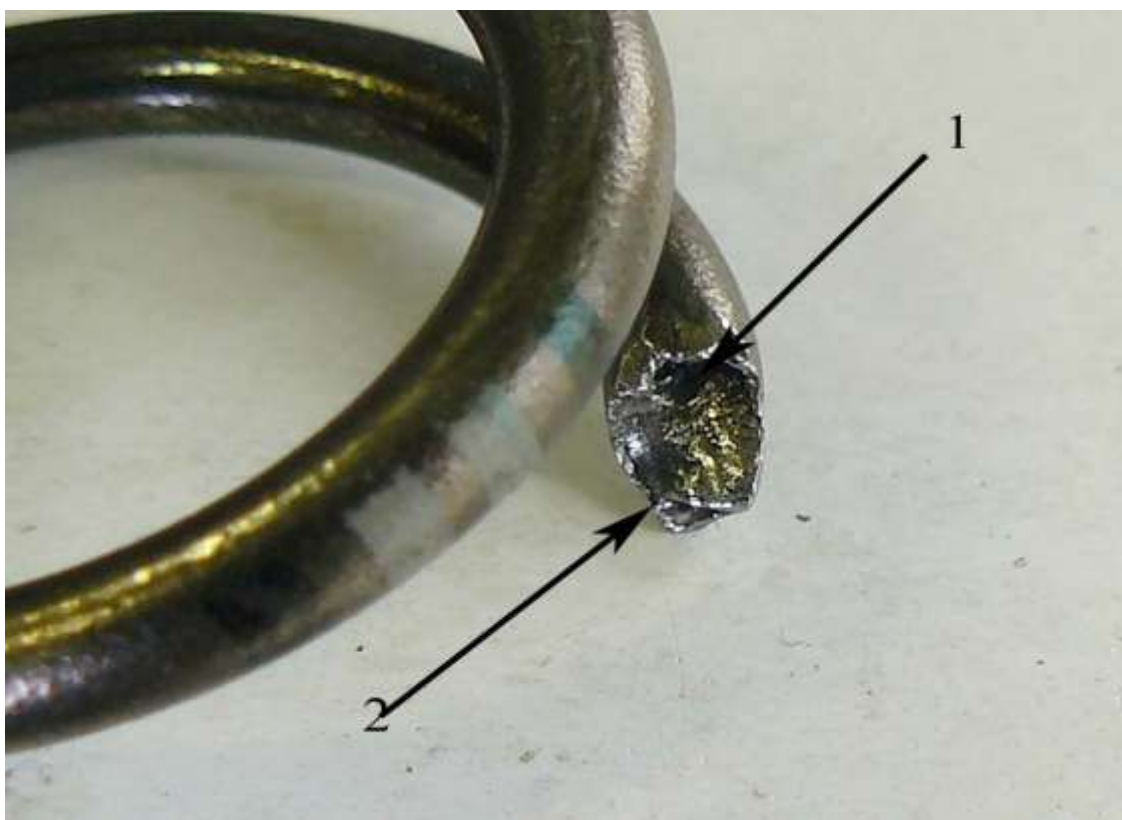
Поверхность излома внешней пружины: 1 — зона образования усталостных трещин; 2 — зона долома
